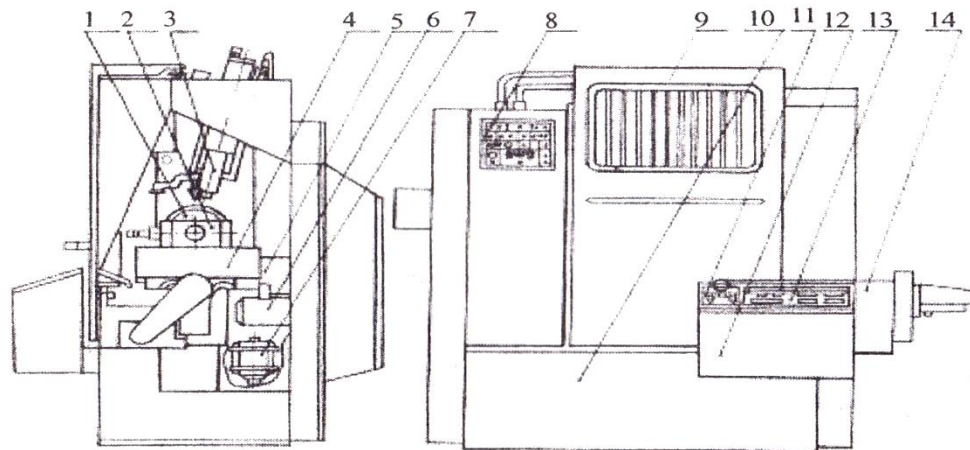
Загальний вигляд верстату 1В340Ф30
